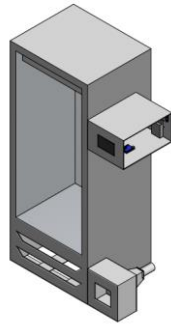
4. *Diseño enfriador vista frontal izquierda
